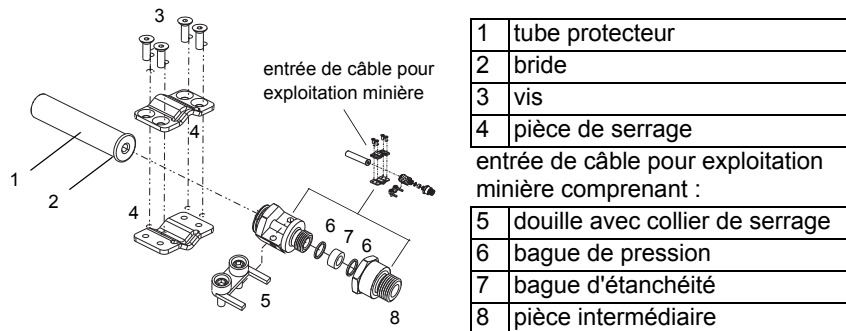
Presse-étoupe M16 pour exploitation minière
